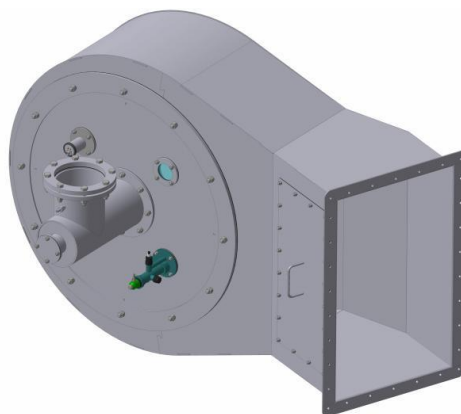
Внешний вид горелки ГГРУ-4500
